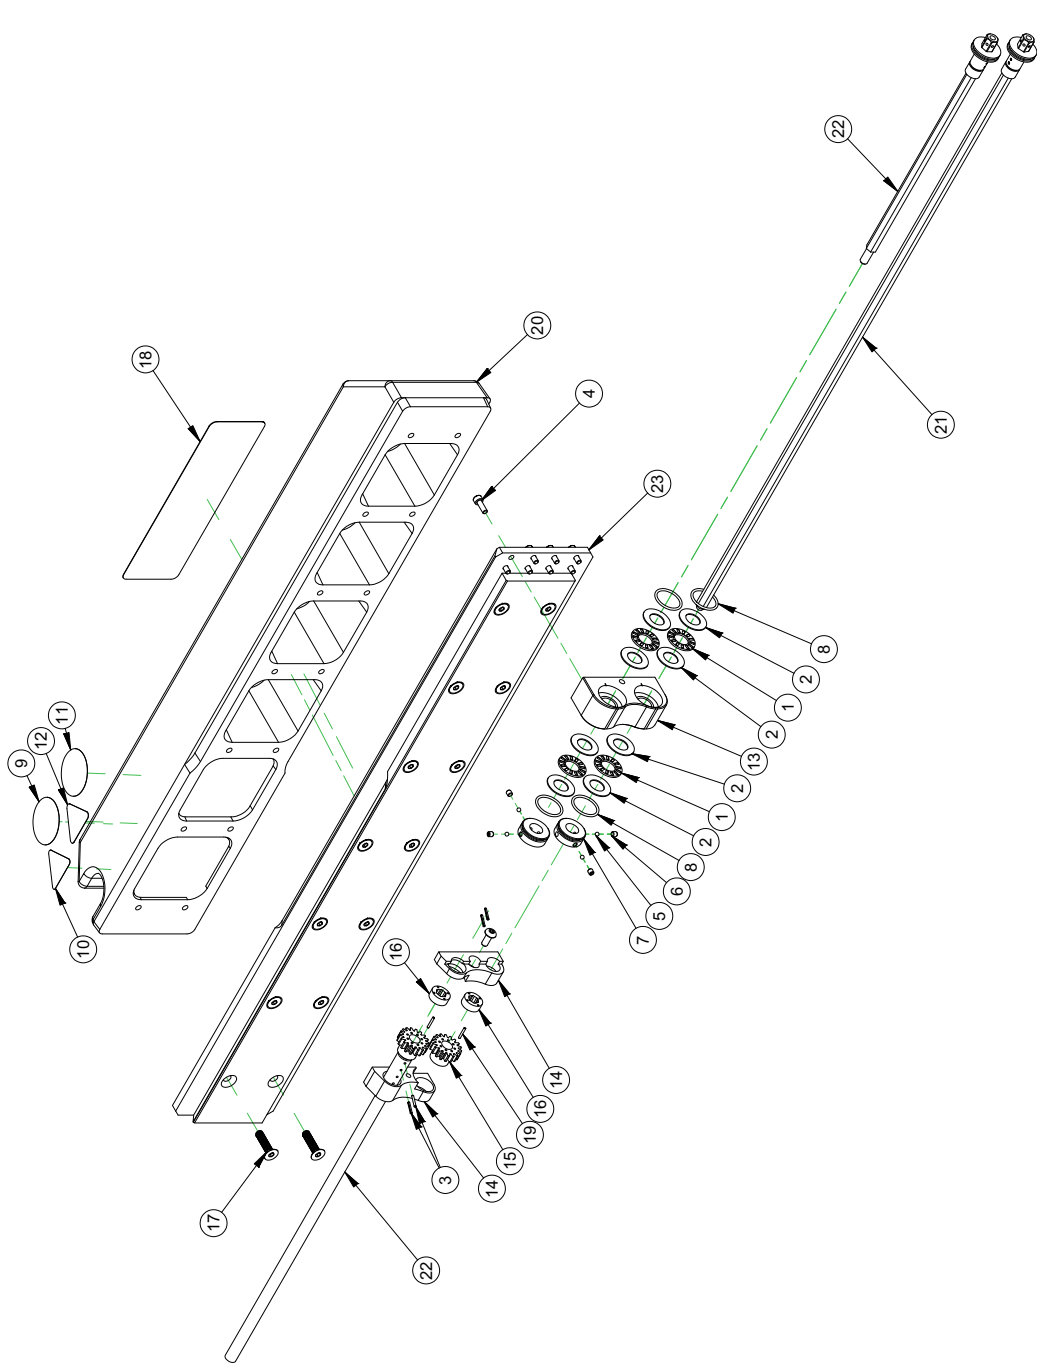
MONTAJE DEL BRAZO DE MECANIZADO (P/N 90337 REVISIÓN D)
